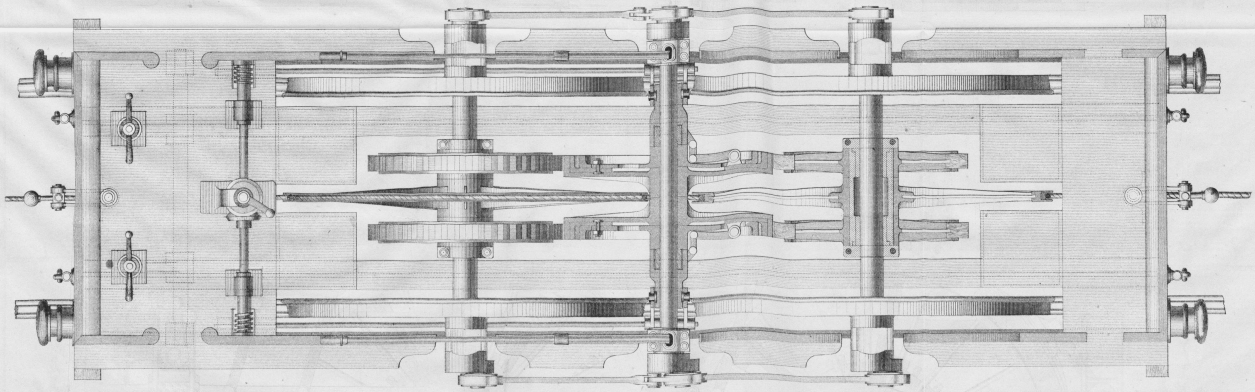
PLAN et COUPE horizontale sur un des essieux
